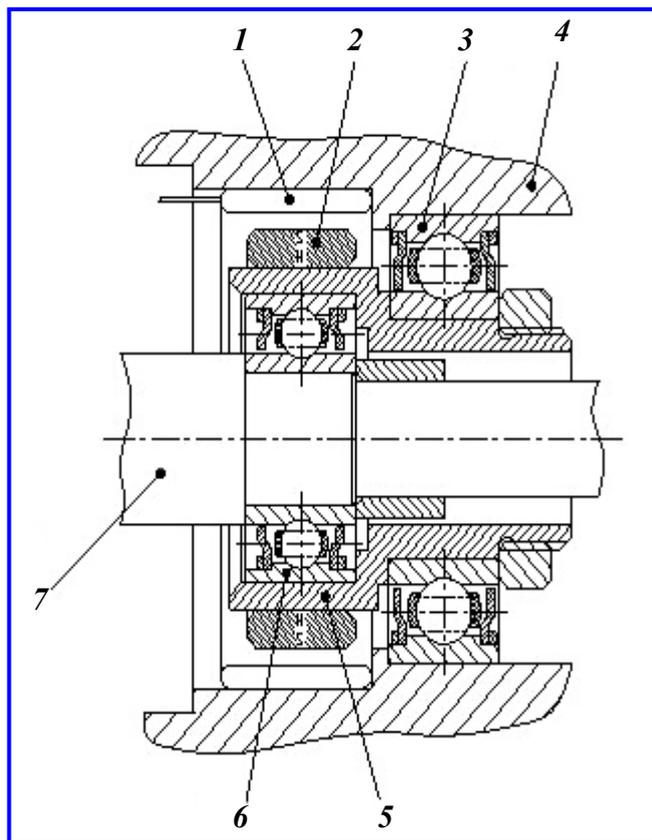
Конструкция опоры качения для устройств, работающих в качательном режиме: 1 – статор миниатюрного встроенного электродвигателя; 2 – магниты миниатюрного встроенного электродвигателя; 3 – вспомогательный подшипник; 4 – корпус устройства; 5 – переходная втулка; 6 – рабочий подшипник; 7 – вал устройства, совершающий качательное движение
